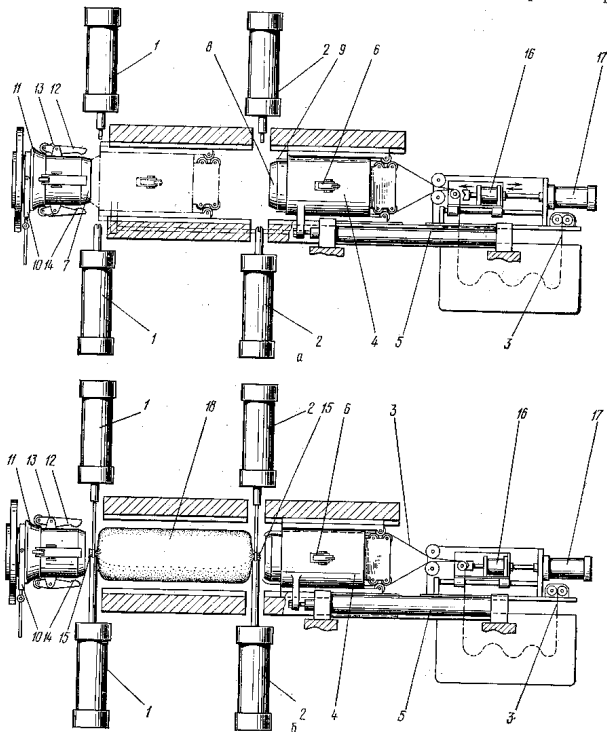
Автомат для изготовления мясoproductов в оболочке:
